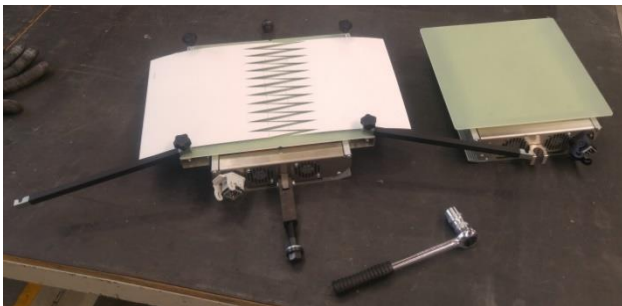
Posición cinta Fabric en placa de unión
